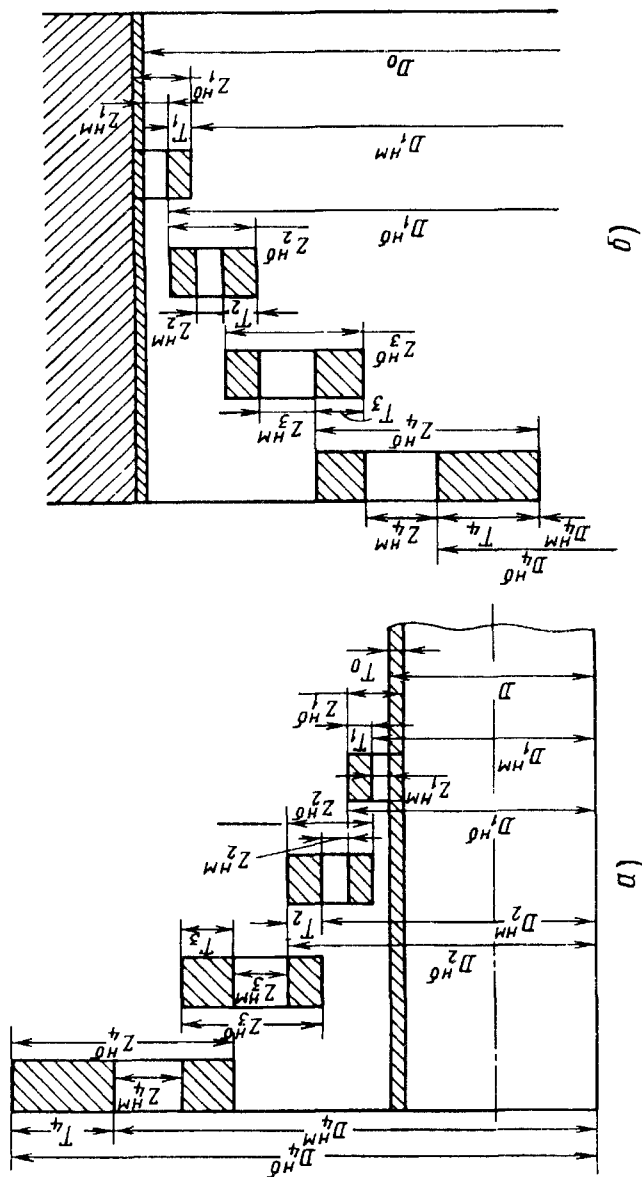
Схемы связей между межпереходными размерами, припусками на обработку и допусками для размера:
